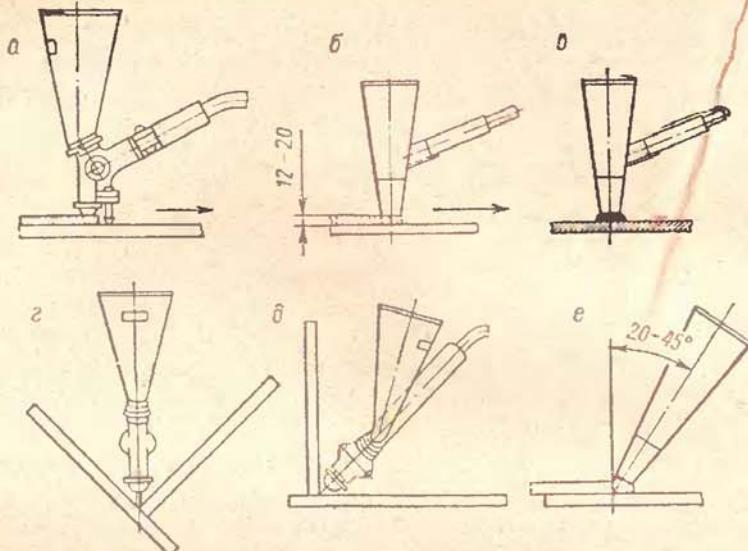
Положение держателя полуавтомата при сварке под флюсом различных соединений:
